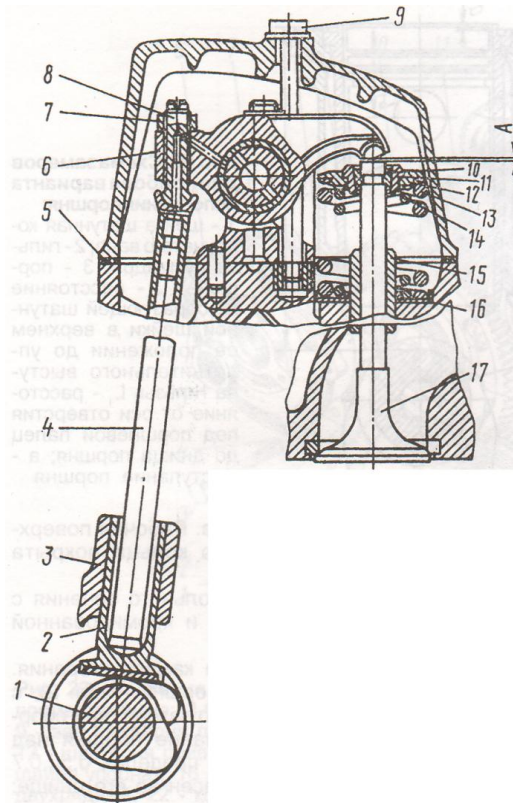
Механизм газораспределения: 1 - вал распределительный; 2 - толкатель; 3 - направляющая толкателей; 4 - штанга; 5-прокладка крышки головки; 6 - коромысло; 7 - гайка; 8 - винт регулировочный; 9 - болт крепления крышки головки; 10 - сухарь; 11 - втулка тарелки; 12-тарелка пружины; 13 - пружина наружная; 14 - пружина внутренняя; 15-направляющая клапана; 16- шайба; 17- клапан; А - зазор тепловой
